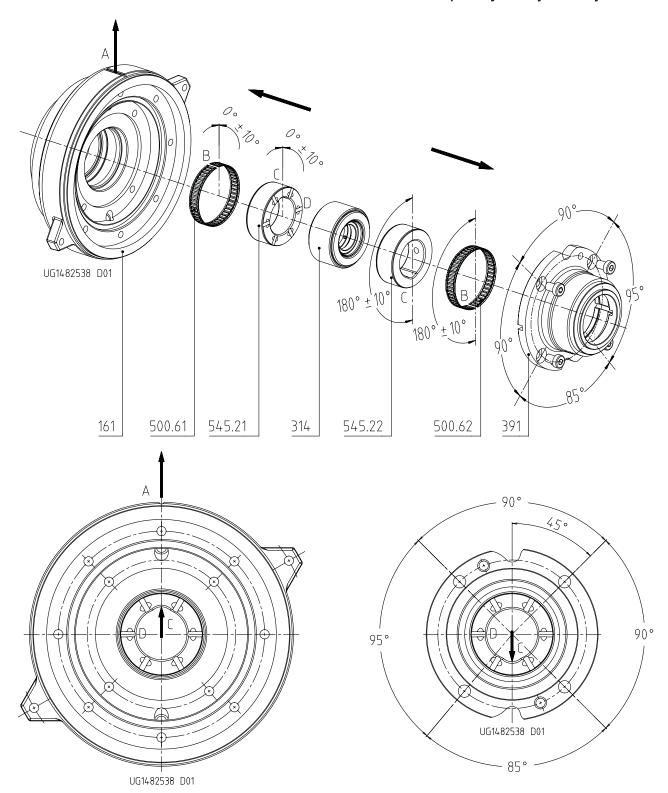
Posicionamiento de los elementos de apriete y los bujes del cojinete con el soporte de cojinetes CS40 / CS50 / CS60
